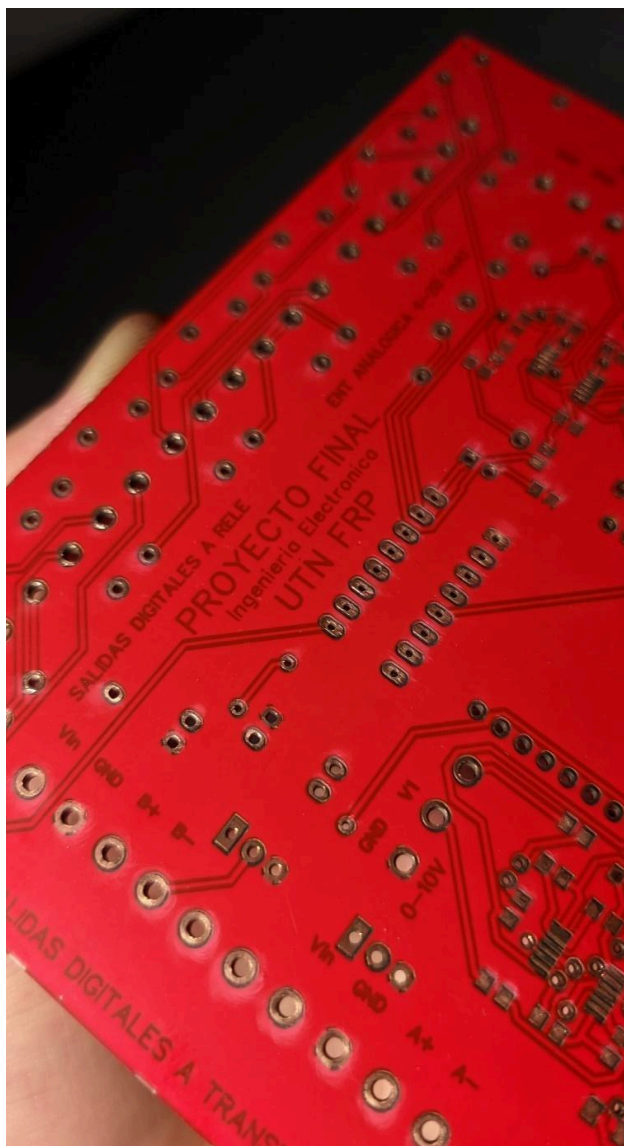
Imagen ilustrativa de vista superior PCB etapa de control.
